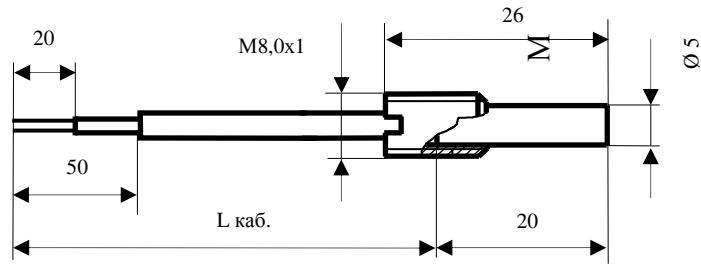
Габаритные и присоединительные размеры ТСП 002-06
